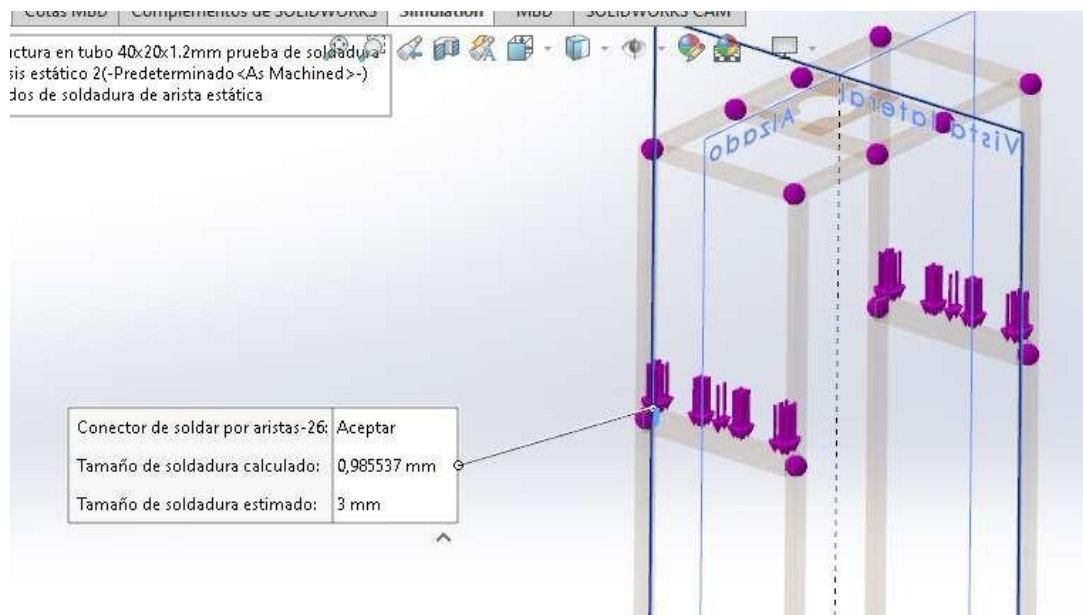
Análisis de cordones de soldadura en puntos críticos. Autoría propia
